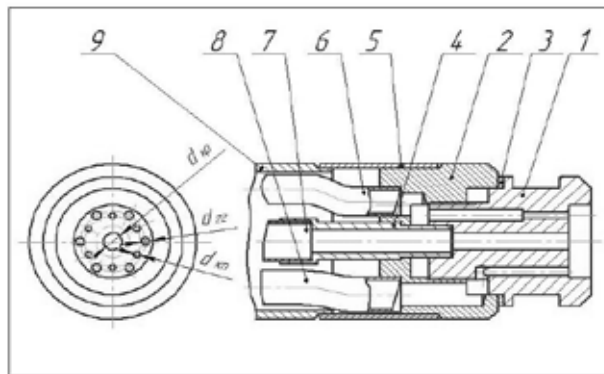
Головка резака РГКМ-6С для резки слитков непрерывного литья толщиной 400-700 мм
